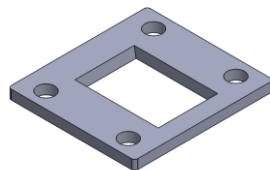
Dimensión de la placa para la movilidad en el plano frontal
